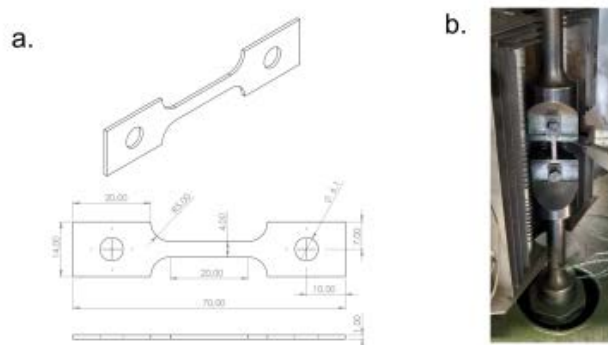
a. Dimensions des éprouvettes usinées par électro-érosion par fil pour les essais de traction à chaud. b. Installation d'une éprouvette vissée dans les mors.
